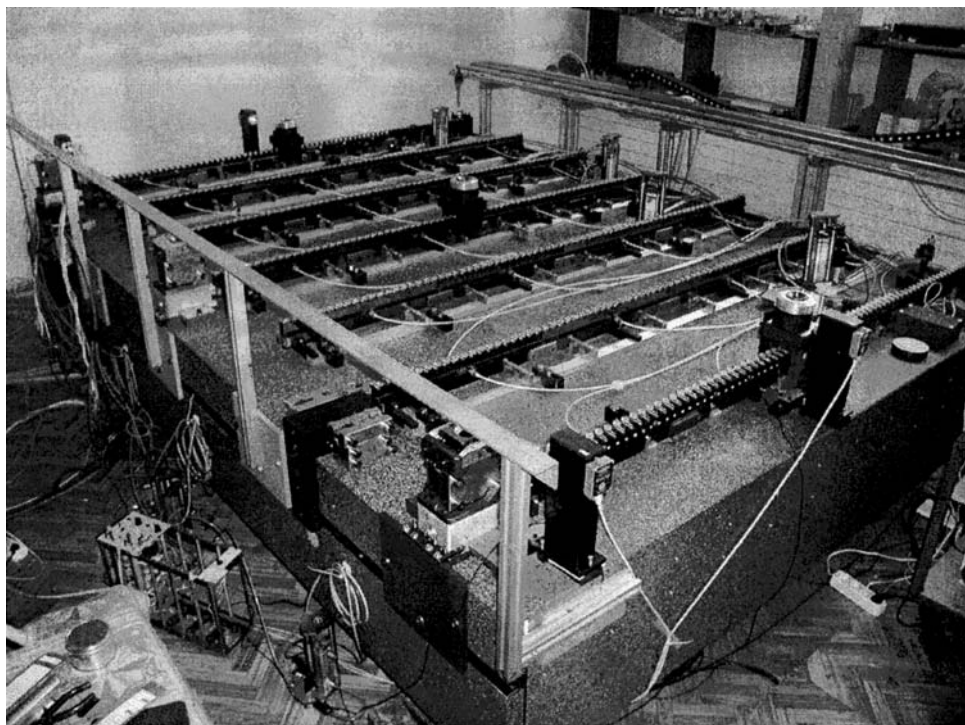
Гранитный стол с семью опорными линиями для сборки камер. Из [255]
